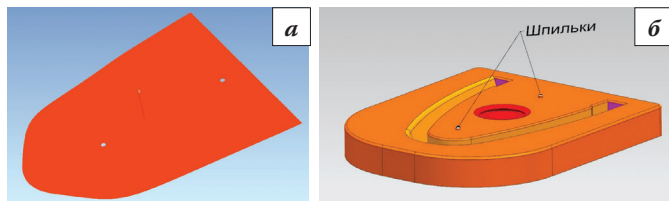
Развертка с отверстиями для шпилек и положение шпилек на оснастке: а – заготовка с припусками; б – шпильки на оснастке
